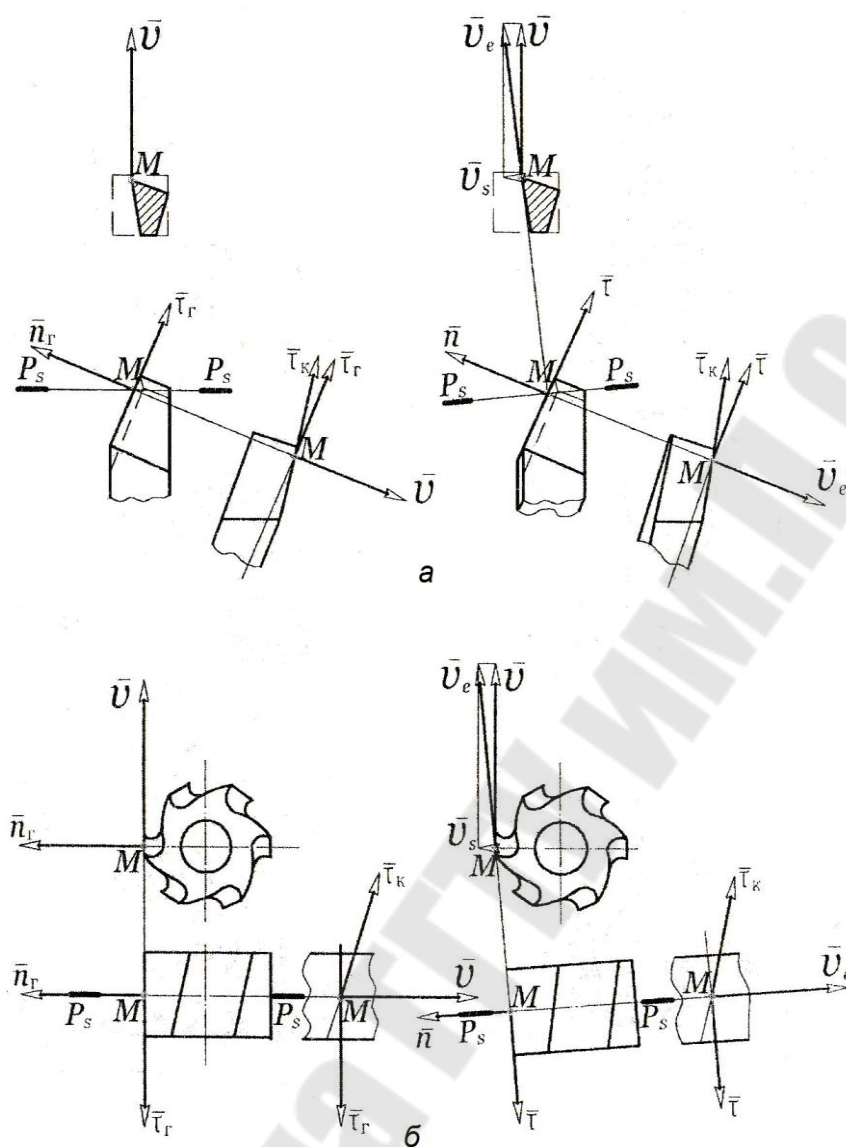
Расположение направляющих векторов относительно поверхности главного движения и поверхности резания для токарного проходного резца (а) и периферийной цилиндрической фрезы (б)
